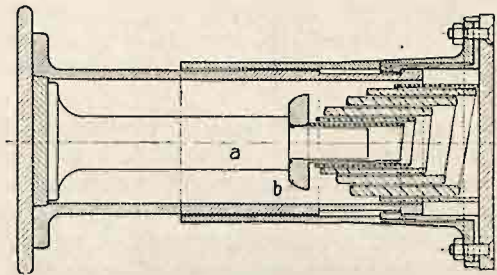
Pierwotny zderzak tulejowy typu Siegen.
